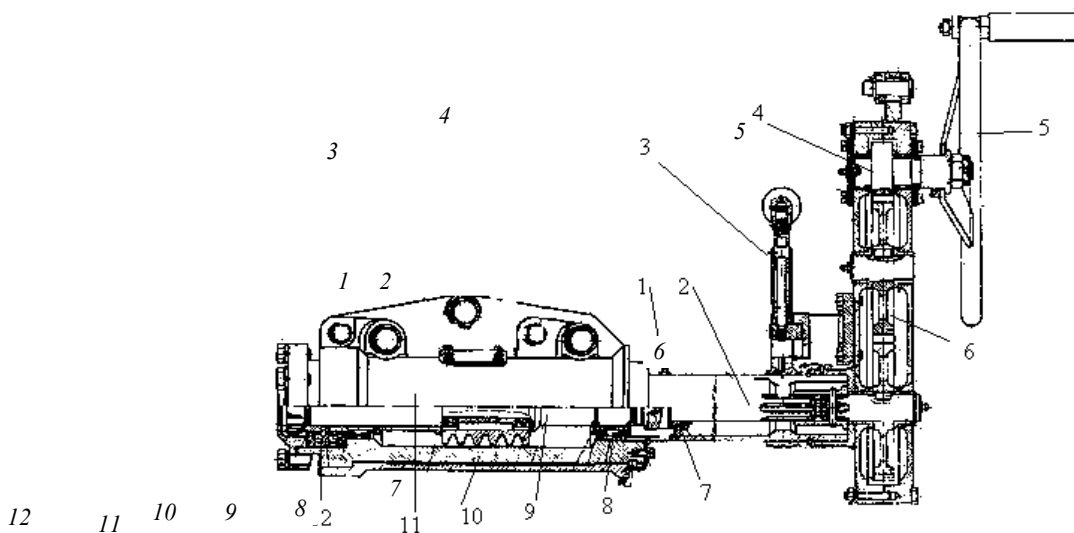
Поворотный механизм 122 мм гаубицы Д-30
